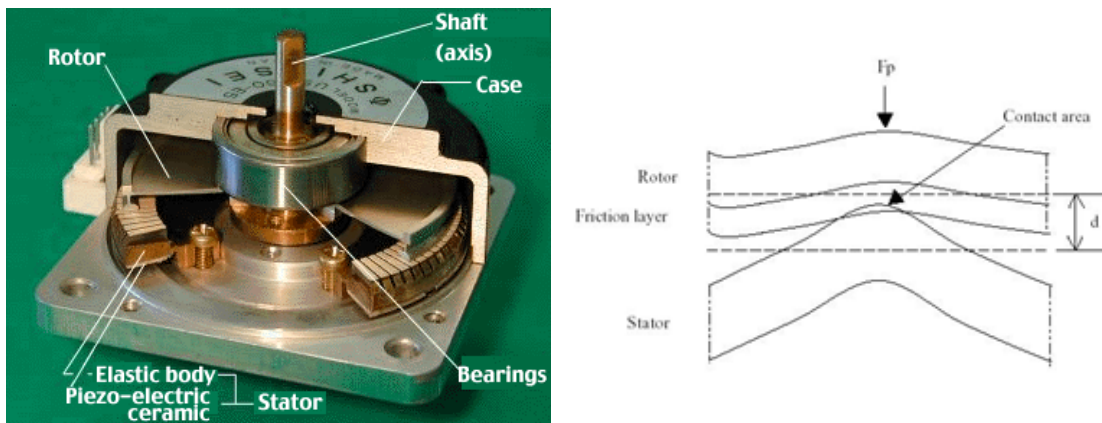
Motor ultrasónico. Izqda. despiece sobre montaje físico. Dcha. detalle de transmisión de par mediante contacto.
